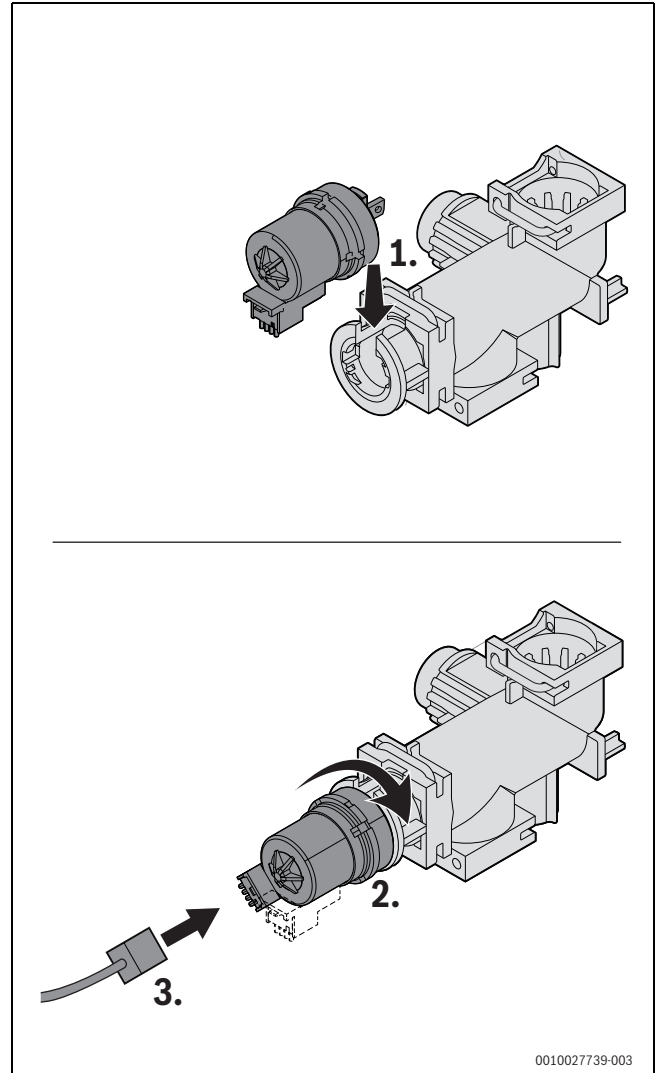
Motor am 3-Wege-Ventil einbauen (Variante ohne Schrauben)
